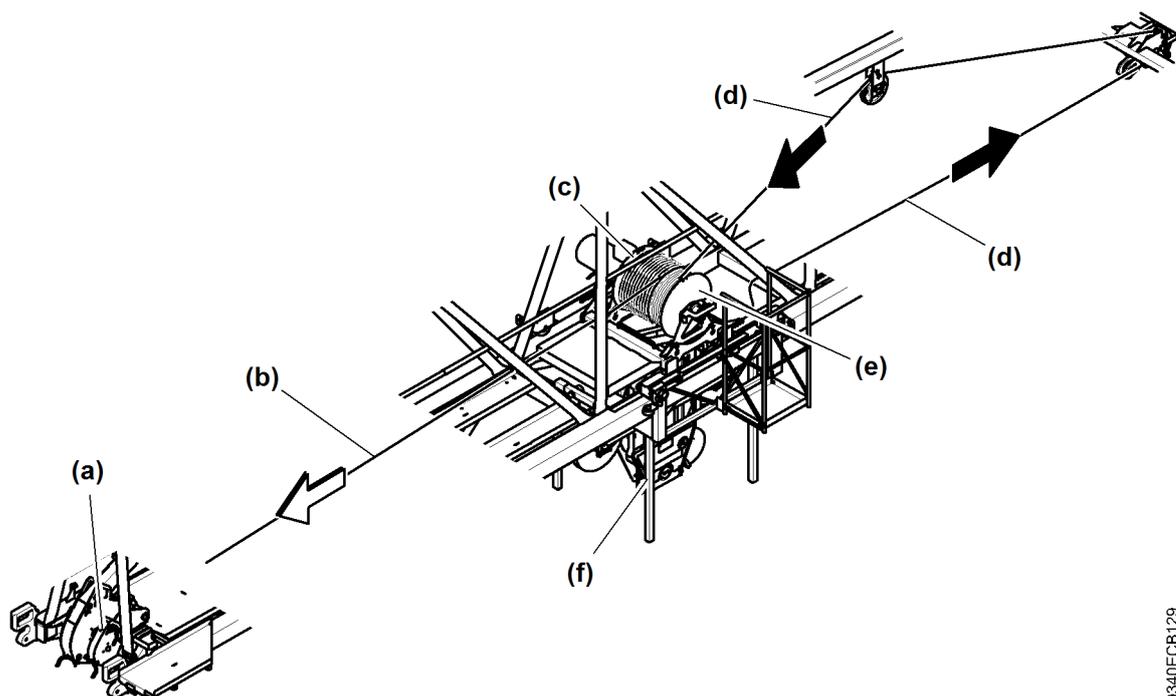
Katzfahrseil I von Seiltrommel abziehen bei Ausleger 75 m oder kürzer
